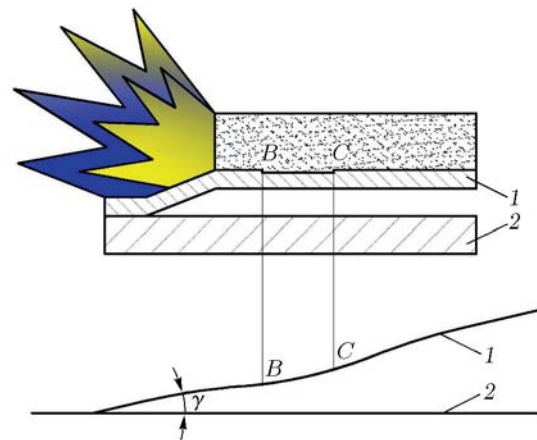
Схема сварки и профили поверхностей соударения:
